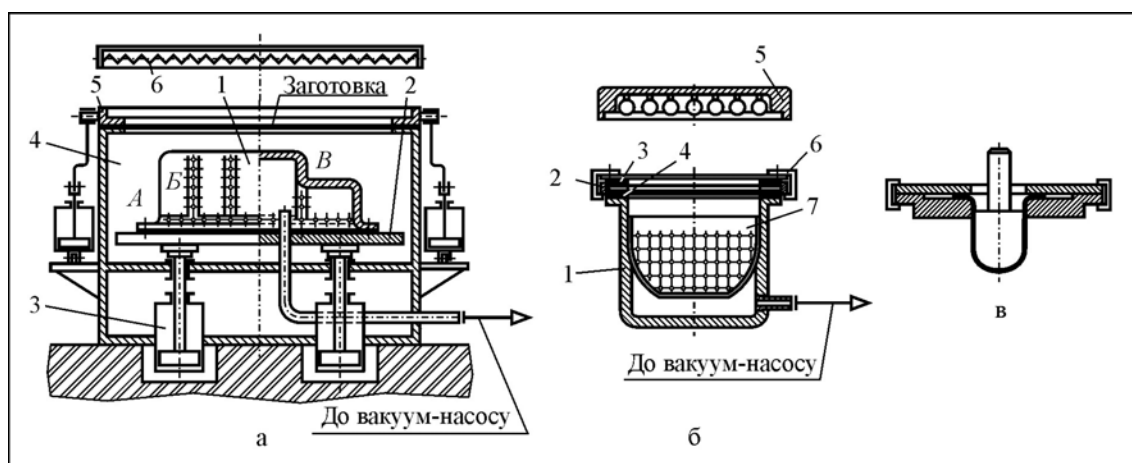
Схеми вакуум-формуванняльних установок (а, б) та схема штампа (в) для виготовлення деталей із листових пластмас
